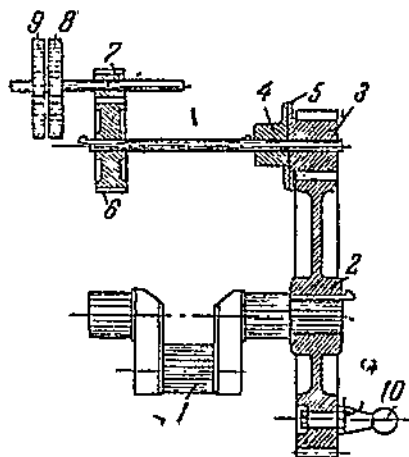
Схема соединения коленчатого вала пресса с приводом:
